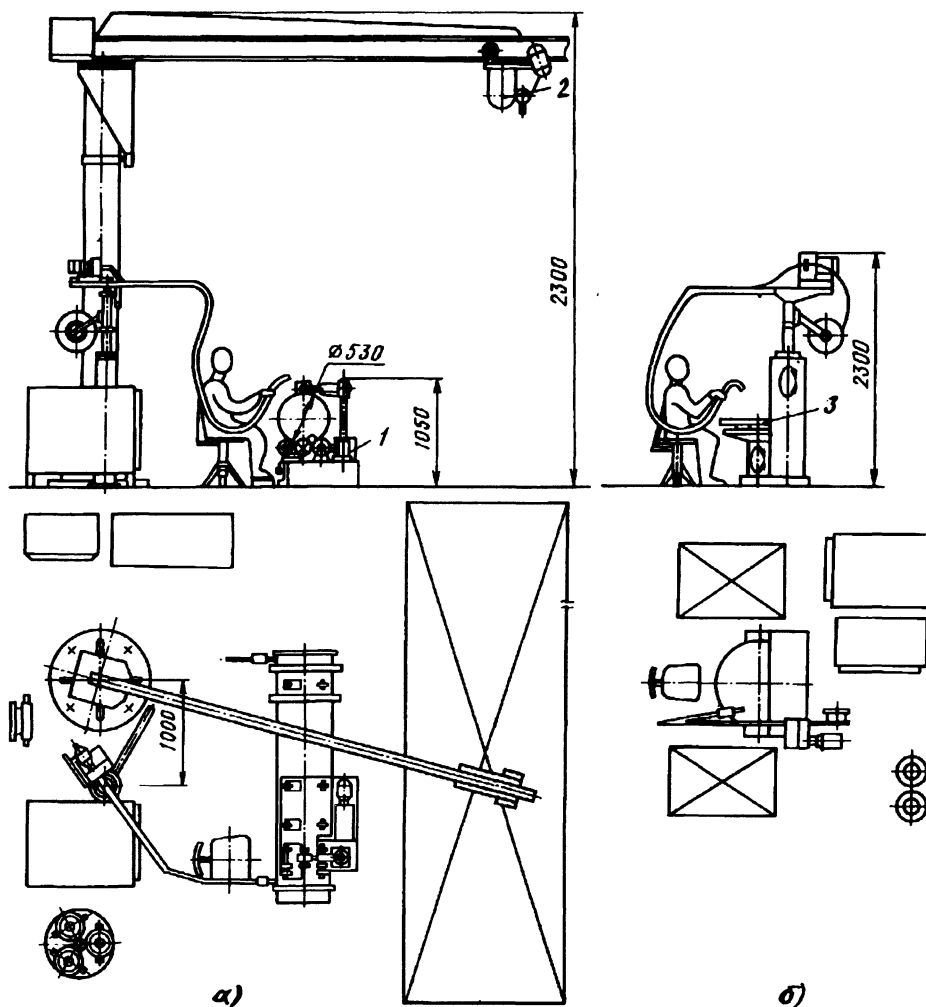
Типовое комплексно-механизированное рабочее место:
